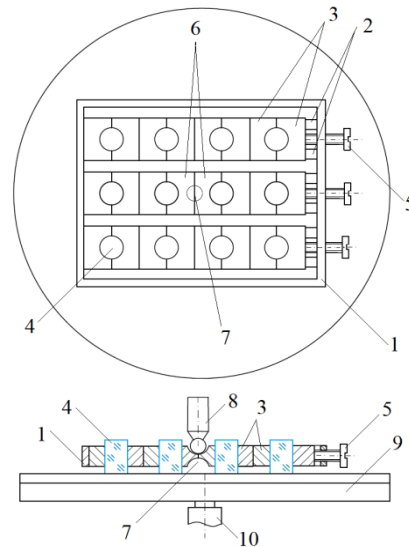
Устройство для шлифования и полирования оснований заготовок цилиндрической формы
